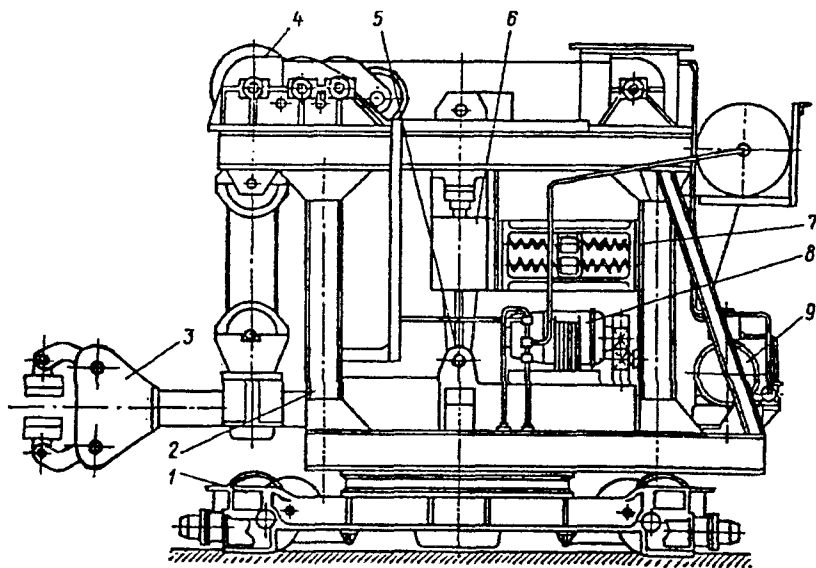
Напольный полноповоротный кузнечный манипулятор
